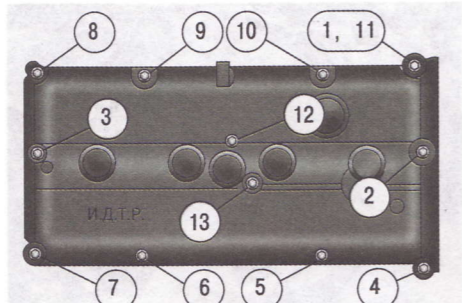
Порядок затяжки болтов крепления крышки головки блока цилиндров
